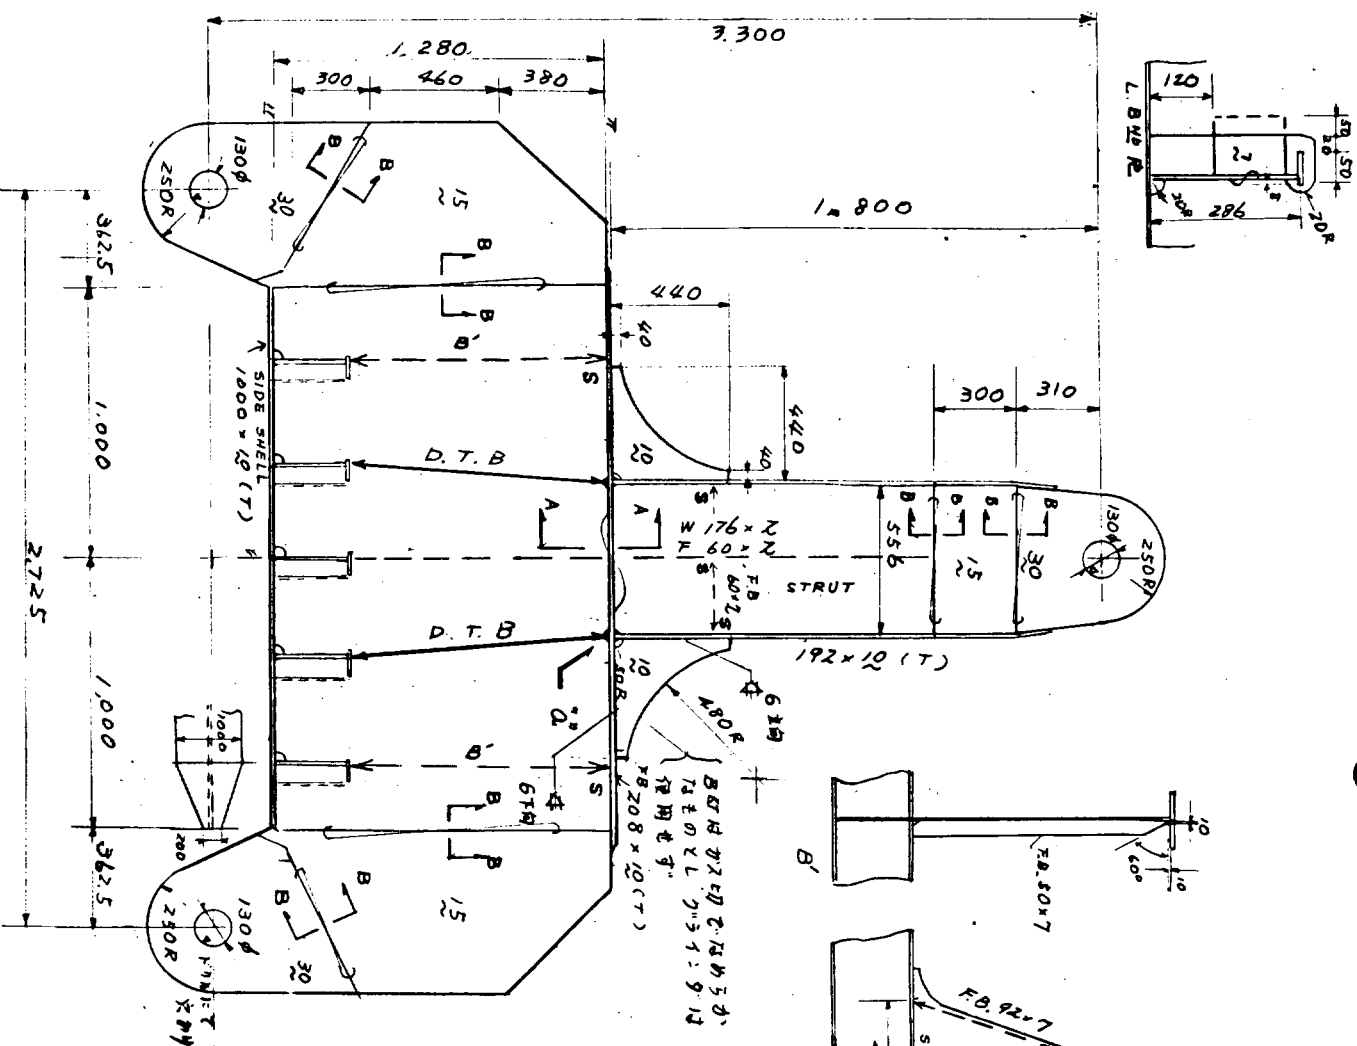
大型試験体 (実船の1/2.5 縮尺) (STRUT 基部)
